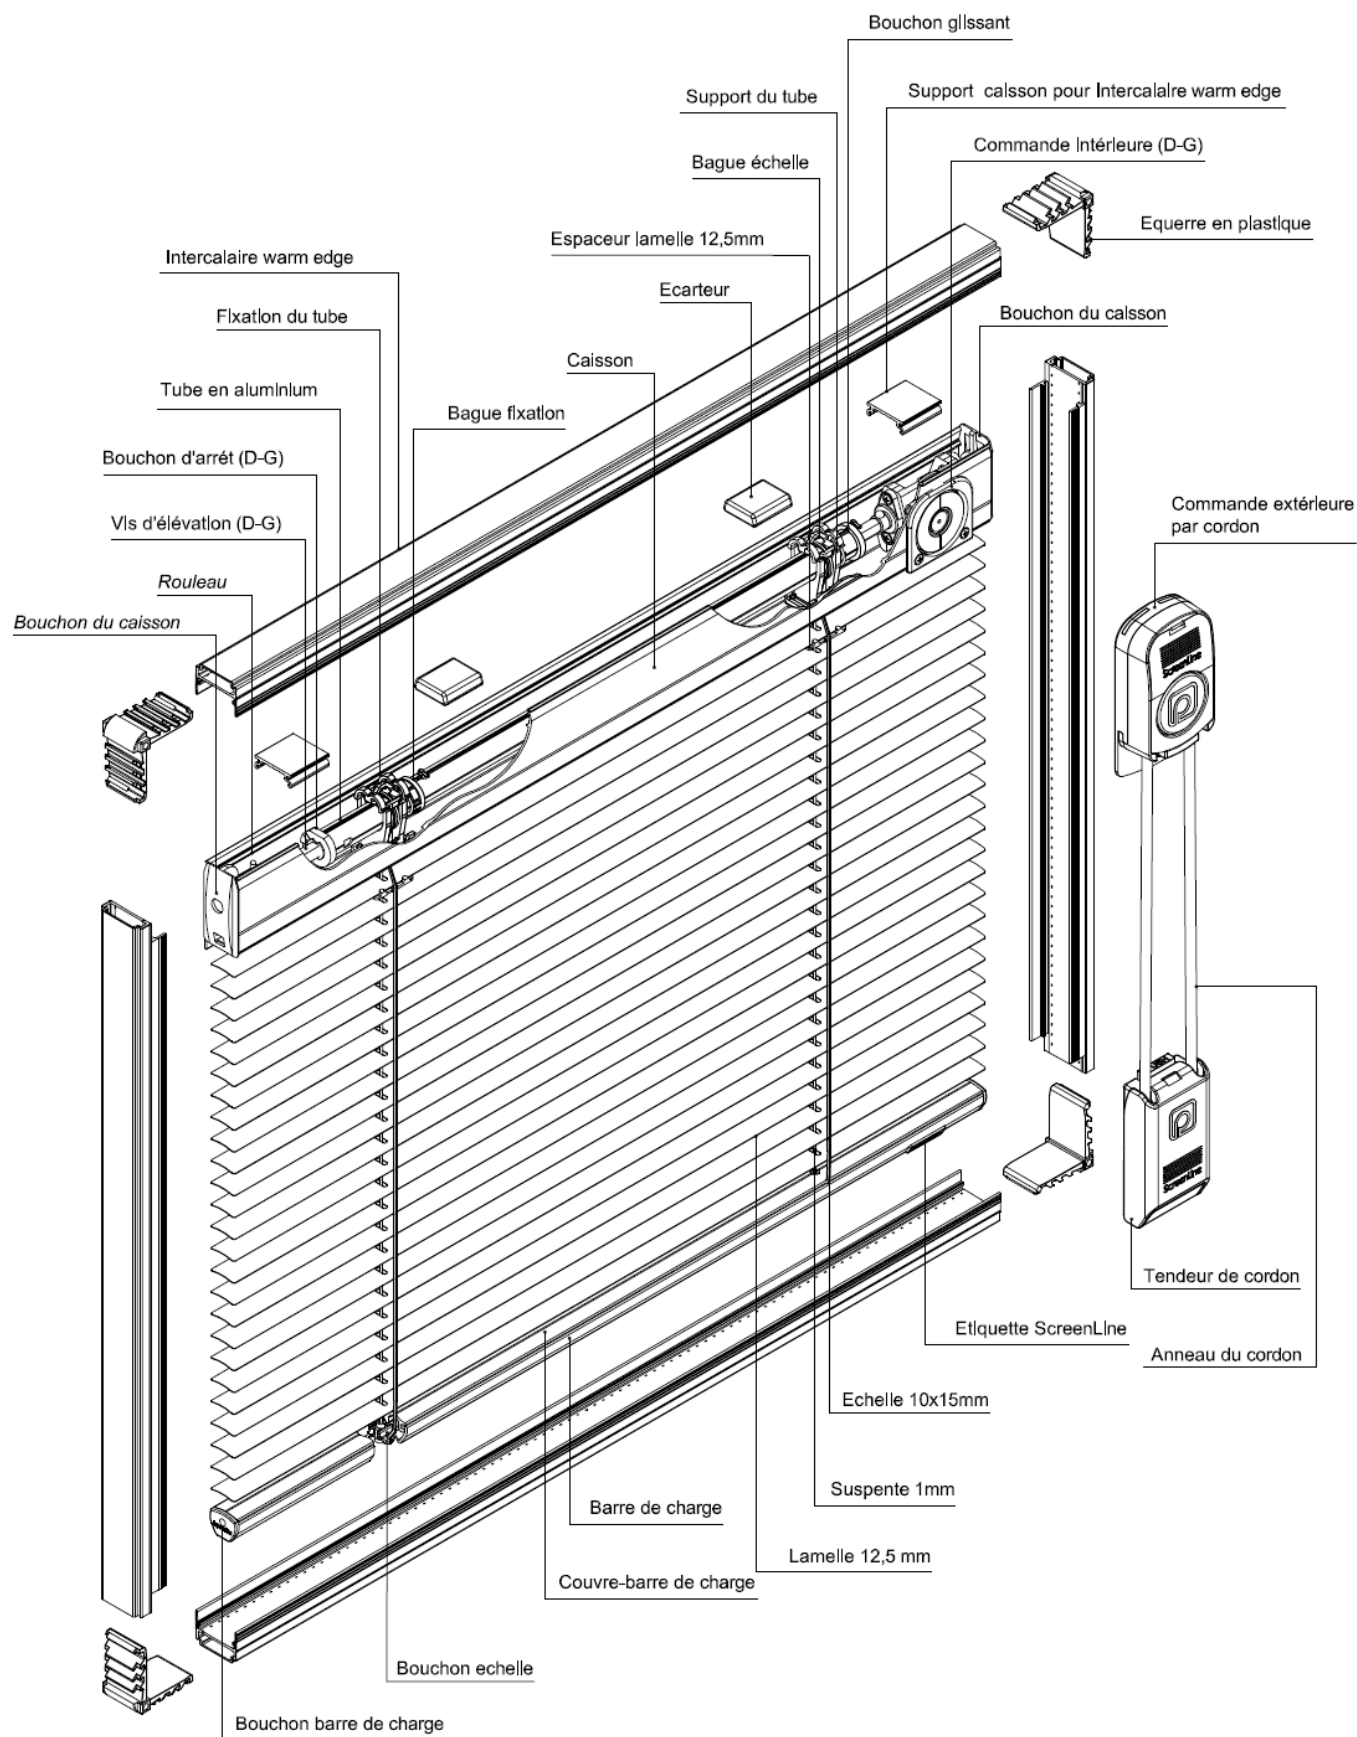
a – Vue d'ensemble éclatée – Store avec espaceur aluminium en position relevée
